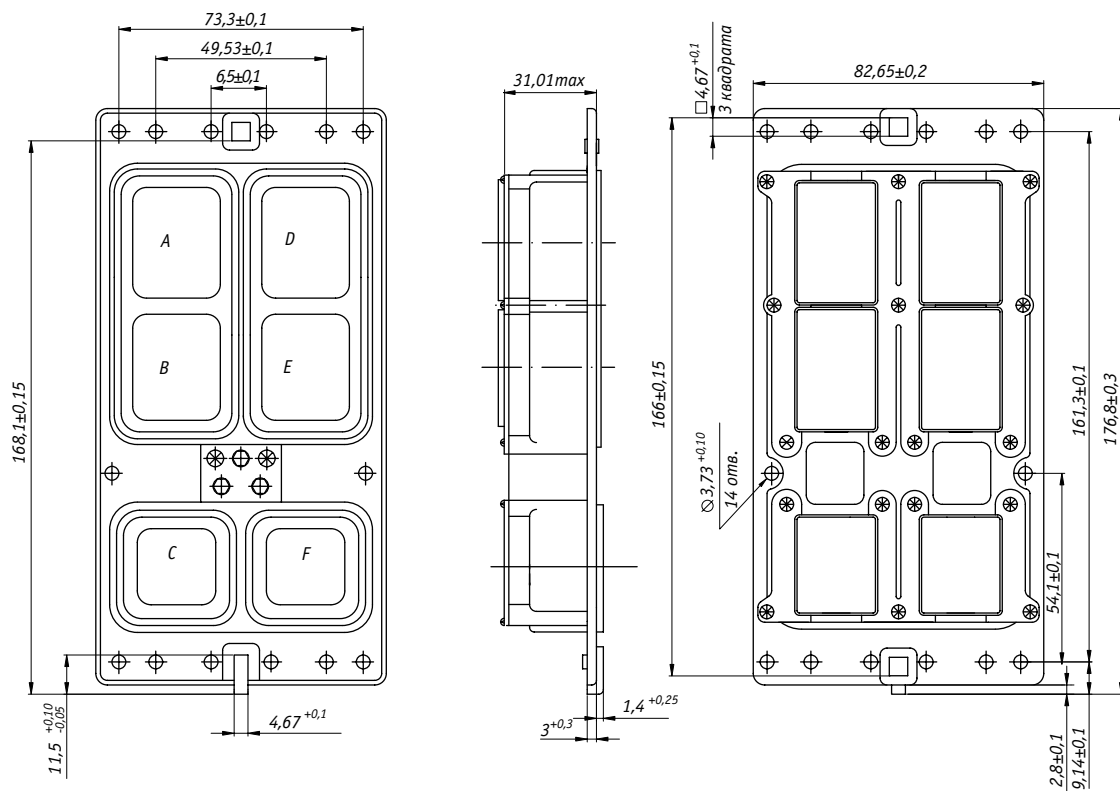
Корпус розеток соединителей 3 типоразмера
